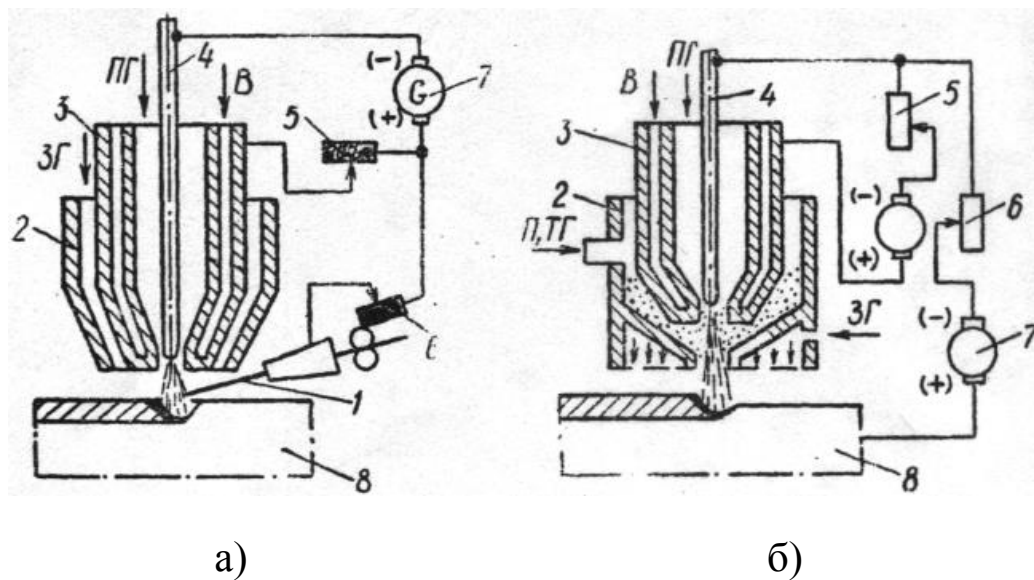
Схема плазово-дугового наплавлення присадним дротом (а) і металічним порошком (б).
